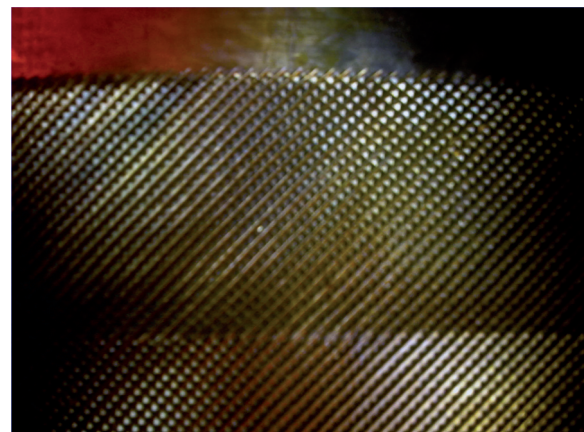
Внешний вид рабочей поверхности грибовидного валка прошивного стана
